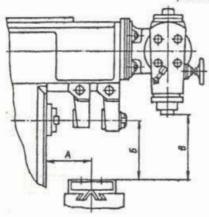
Базовые и присоединительные размеры хобота и серьги (в скобках размеры для станка 6Т83Ш)
